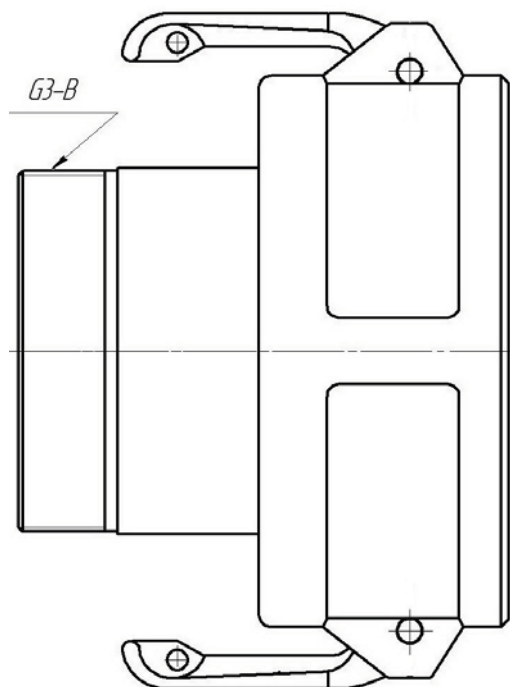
Муфта клапана паровозврата без обратного клапана с резьбой G3 для установки БРС и присоединения рукава отвода паров
